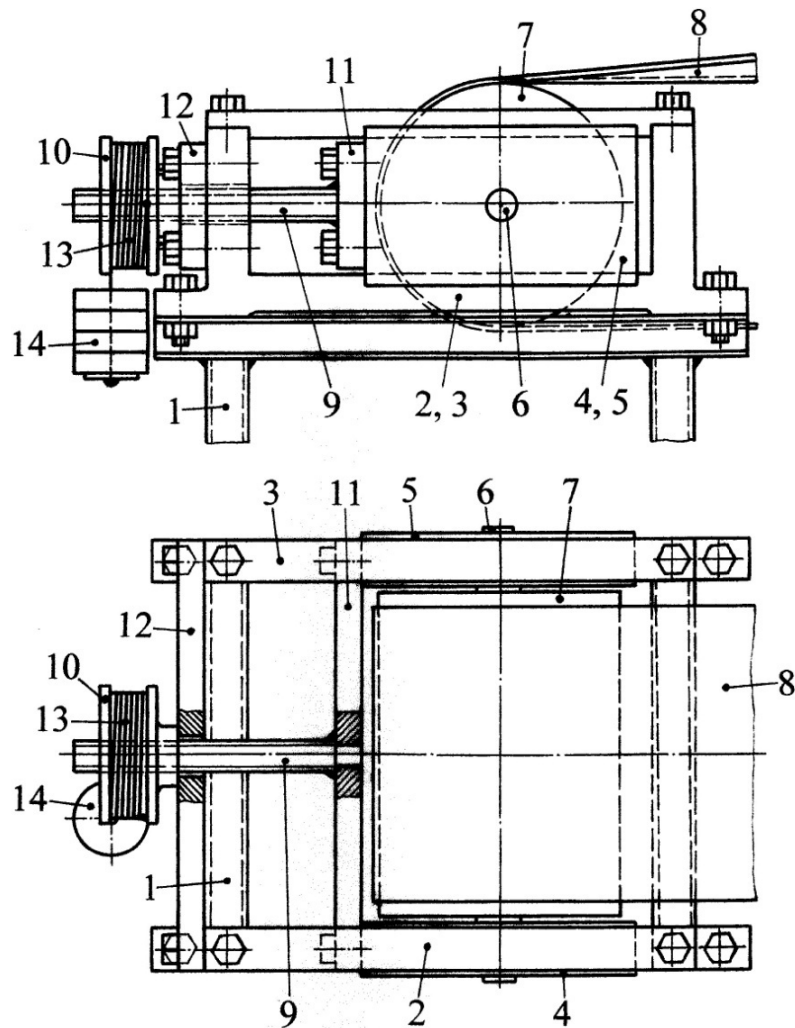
Схема удосконаленого гвинтового пристрою стрічкового конвеєра: 1 – рама; 2, 3 – напрямні; 4, 5 – повзуни; 6 – вісь; 7 – натяжний барабан; 8 – стрічка; 9 – натяжний гвинт; 10 – дискова гайка; 11, 12 – жорсткі пластини; 13 – гнучкий трос; 14 – підвісний вантаж
